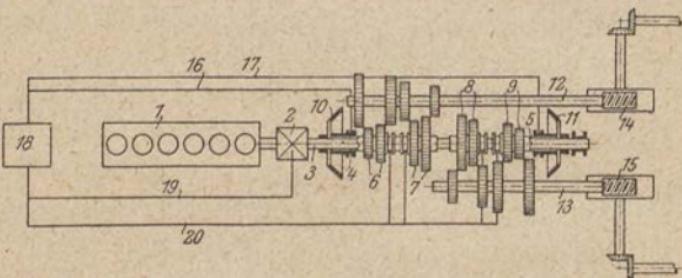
Getriebe mit zwei Wechselräderwerken (Grundriss).
